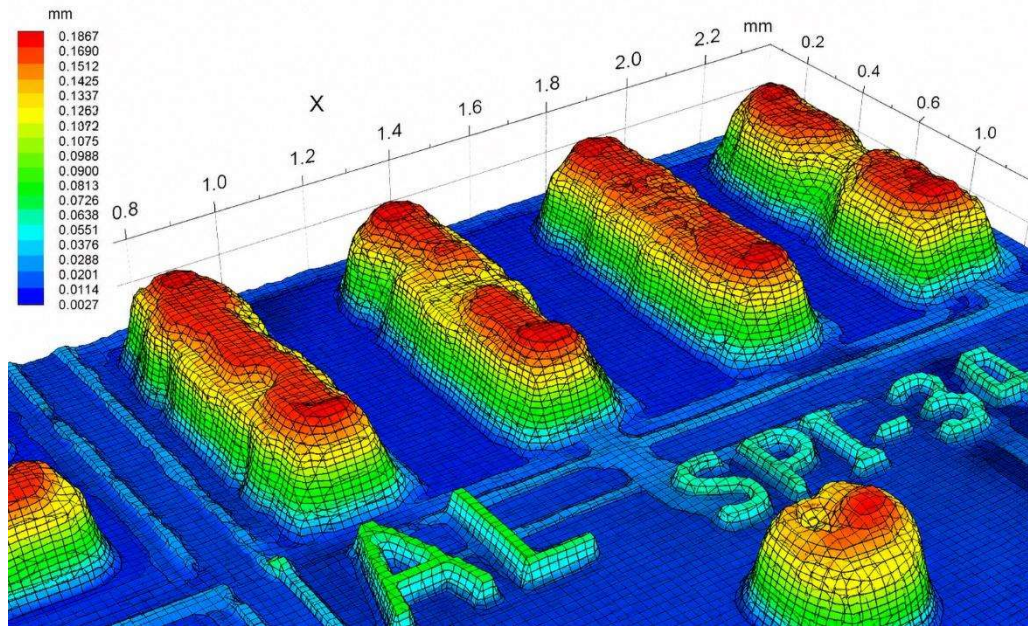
Ejemplo de inspección de soldadura 3D.
